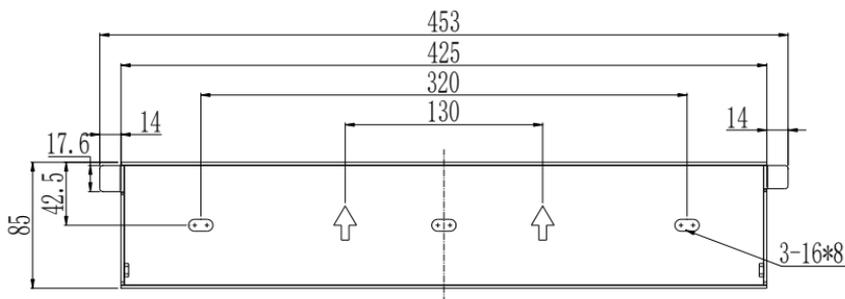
Dimensioni piastra di fissaggio del R5-17K/20K-T2
